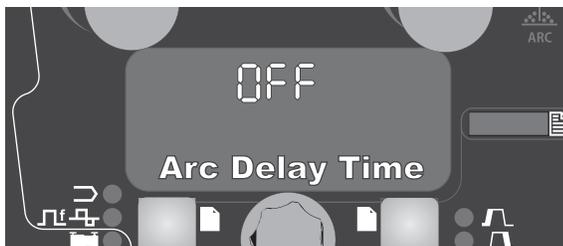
SECUENCIA DE SOLDADURA
